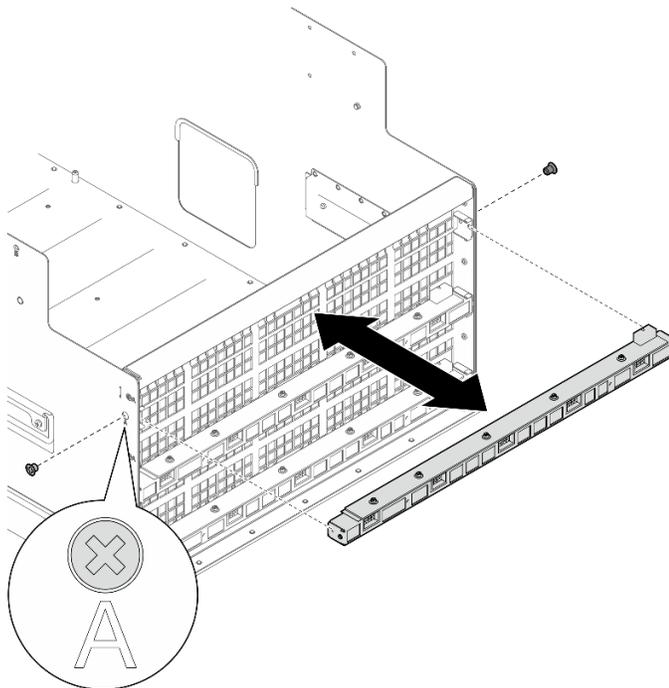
Remoção do conjunto de placa de controle do ventilador traseiro
